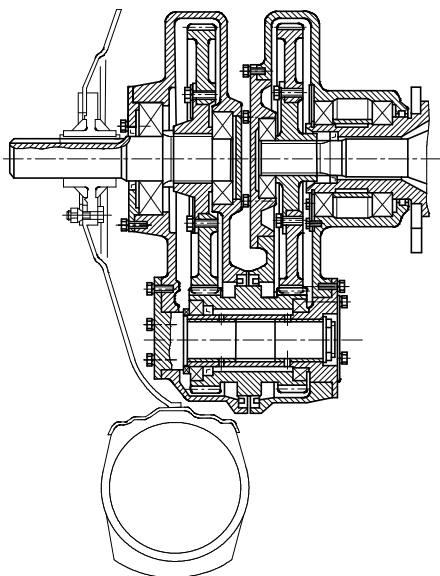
Конструкция сдвоенного бортового редуктора в разрезе
